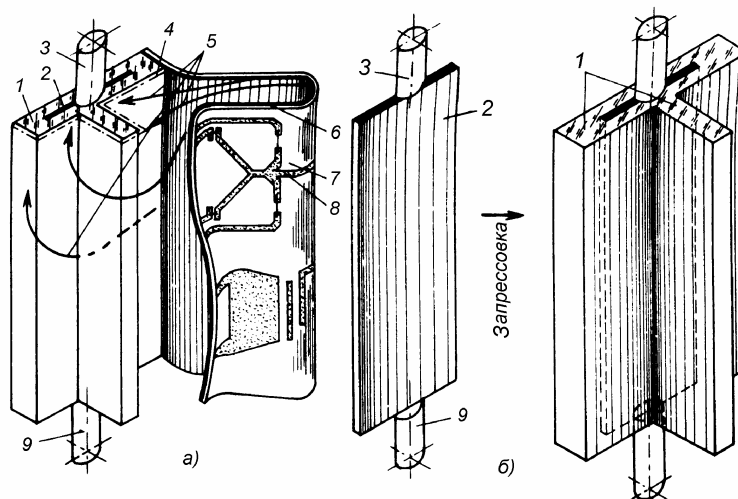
Схемы сборки РДОС (а) и изготовления диэлектрической оправки РДОС (б): 1 — фторопластовая Т-образная оправка; 2 — металлический пластинчатый каркас; 3, 9 — металлические фиксирующая и установочная оси каркаса; 4 — контур выклейки ГДП; 5 — направление выклейки ГДП; 6 — ЭСМ; 7 — ГДП; 8 — схемный ПЭ
